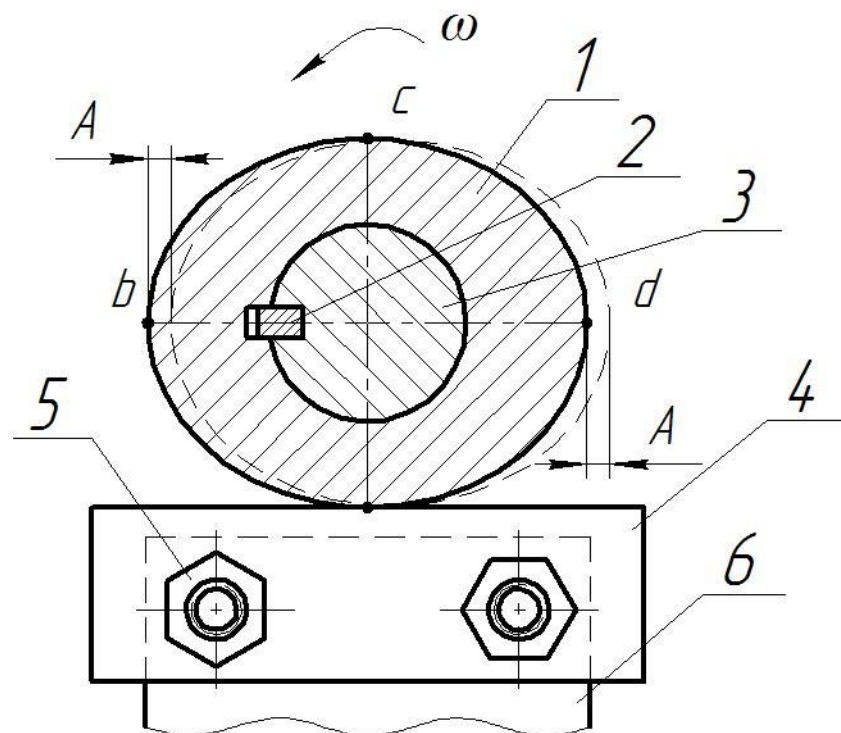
Профиль кулачка, моделирующий динамическое нагружение виброизолятора: 1- эксцентрик; 2 - шпонка; 3 - вал; 4 - пята; 5 – болт; 6 - центральная пластина виброизолятора
